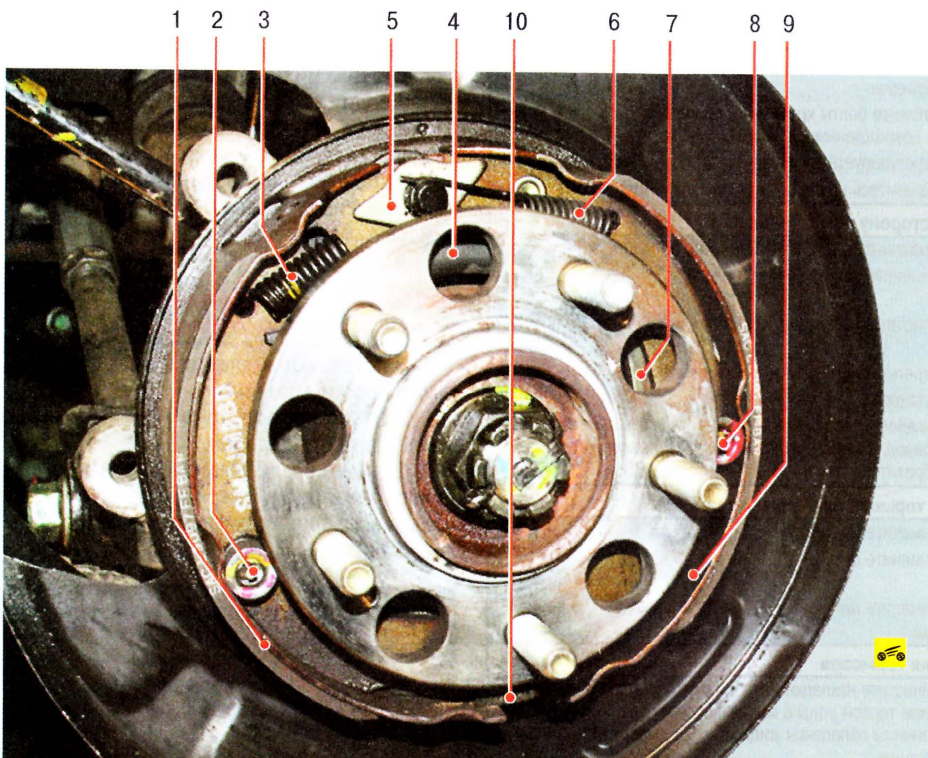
Стояночный тормозной механизм: 1 – передняя колодка стояночного тормозного механизма; 2, 8 – опорные стойки колодок; 3 – верхняя стяжная пружина передней колодки; 4 – распорная планка; 5 – фиксирующая пластина колодок; 6 – верхняя стяжная пружина задней колодки; 7 – разжимной рычаг привода стояночного тормозного механизма; 9 – задняя колодка стояночного тормозного механизма; 10 – нижняя стяжная пружина колодок
